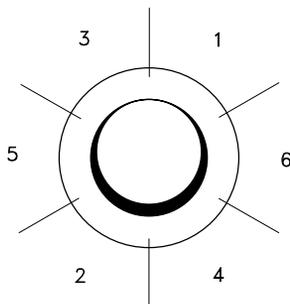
Порядок приварки адаптера к трубе / емкости
